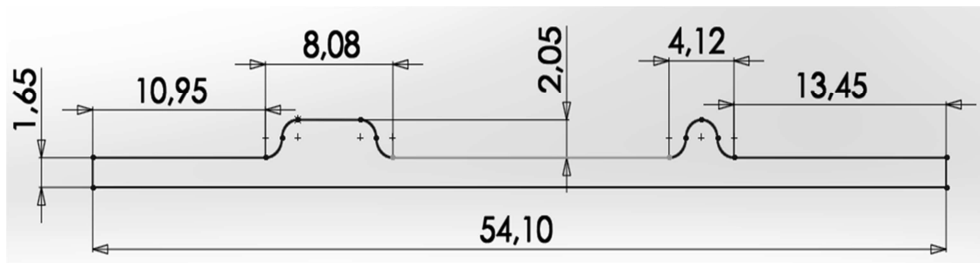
Розгортка поковки з припуском з розмірами (вигляд збоку)
